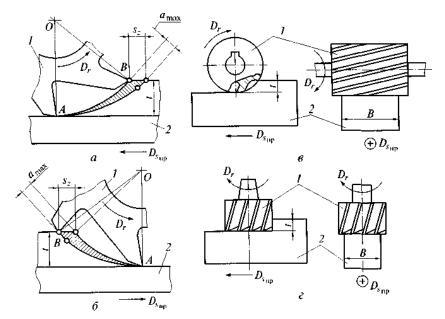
Схемы фрезерования против движения подачи (*a*) и по движению подачи (*б*) цилиндрической (*в*) и торцовой (г) фрезами:
